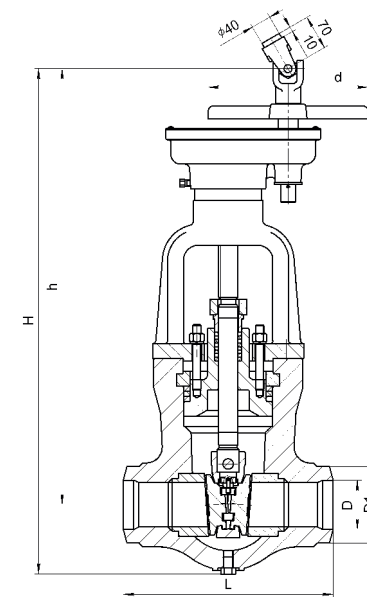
Задвижка DN100 с цилиндрическим редуктором
